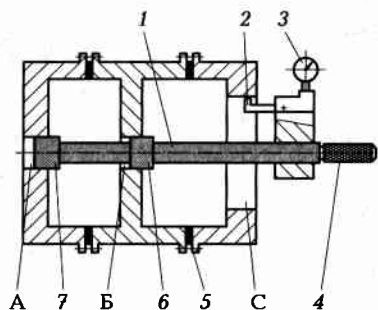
Схема контроля соосности поверхностей индикаторным приспособлением:
